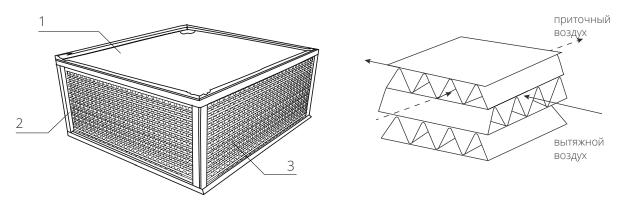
Конструкция пластинчатого перекрестноточного рекуператора PANOVA. 1 – боковая панель, 2 – стойки, 3 – пластины
